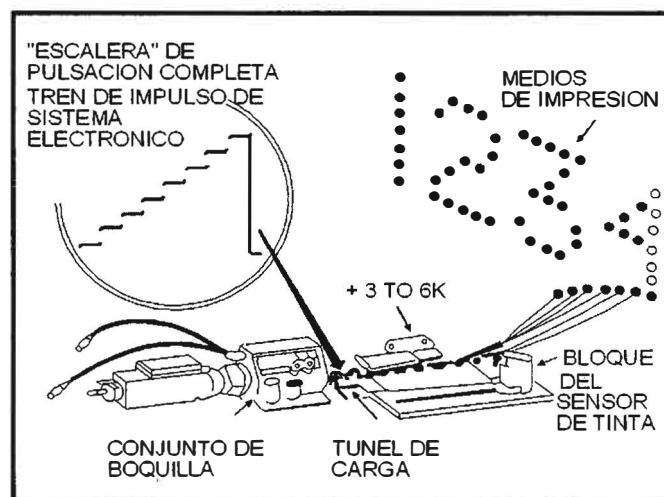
Partes del cabezal de impresión (boquilla) [13]
